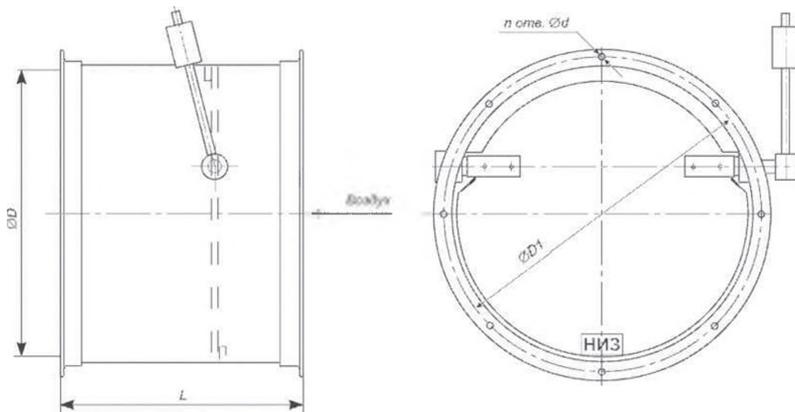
Клапан обратный взрывозащищенный круглого сечения АЗЕ 100.000
